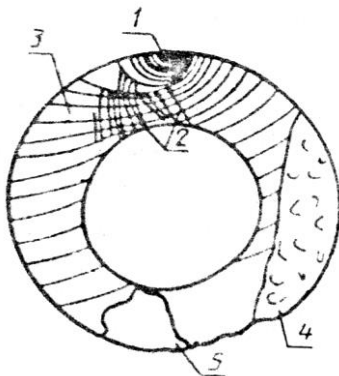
Схема усталостного излома: 1 – очаг разрушения; 2 – ступеньки и рубцы; 3 – усталостные линии; 4 – зона ускоренного развития трещины; 5 – зона долома
